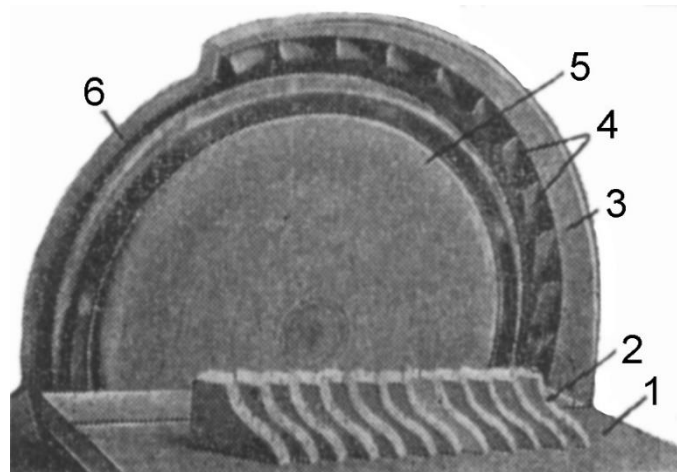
Огороження-порохоприймач дискового шліфувального верстата: 1 – стіл, 2 – виріб, 3 – корпус верхнього порохоприймача та його стінки, 4 – напрямні стінки порохоприймача, 5 – шліфувальний диск, 6 – корпус огороження диска.
